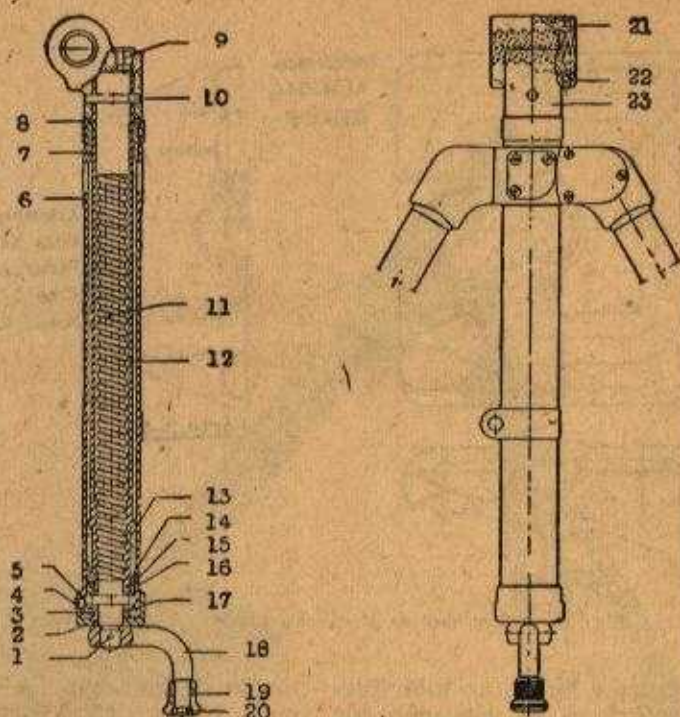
Morteiro de 60 mm — Mecanismo de elevação — Visto seccionado detalhado
